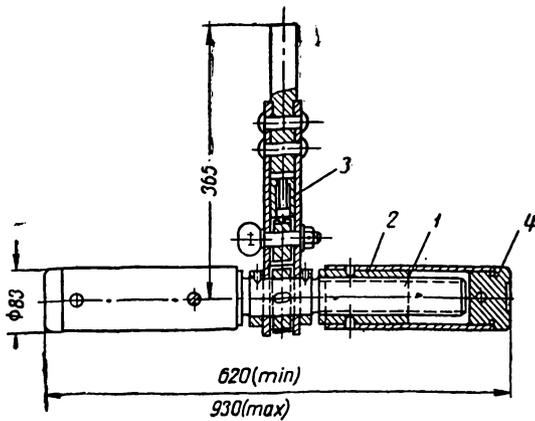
Приспособление для правки кузова вагонеток ниже обвязки
